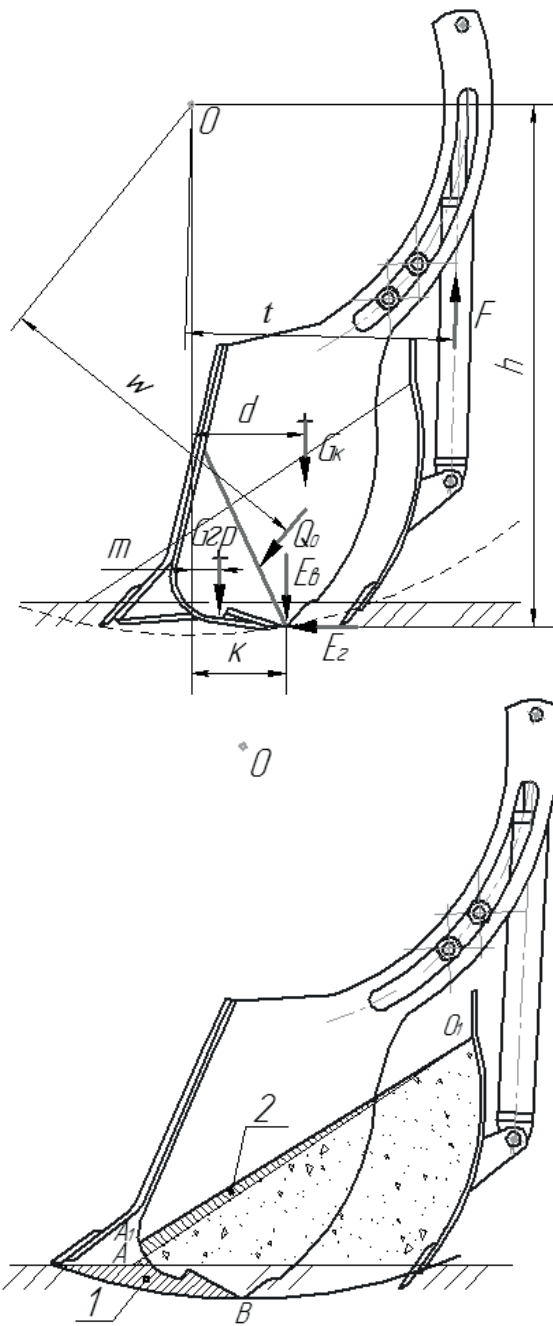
Схемы, используемые при расчете: а – схема для определения усилия на штоке гидроцилиндра, при копании грунта дополнительным отвалом; б – схема размещения выкопанного грунта в ковше
